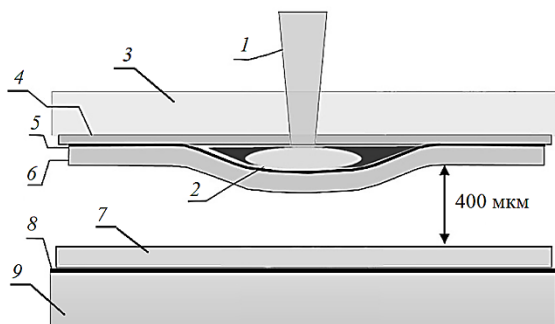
Принципиальная схема технологии ЛУС: 1 – Лазерный луч; 2 – Плазма; 3 – Прозрачный слой (Боросиликатное стекло); 4 – Двусторонний скотч; 5 – Черная краска; 6 – Математическая алюминиевая пластина; 7 – мишень из нержавеющей стали; 8 – черная лента; 9 – подложка
